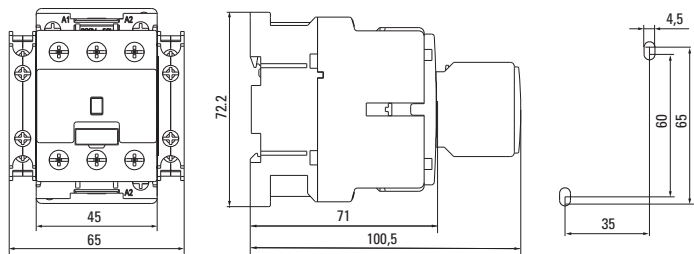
Габаритные и установочные размеры контакторов KM3 25A, KM3 30A
